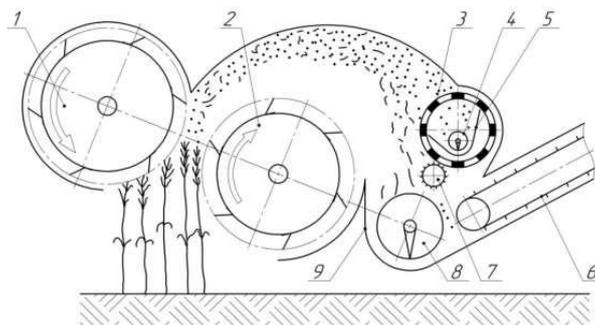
Пристрій для обмолоту рослин на корені: 1 – подаючий барабан; 2 – очисний барабан; 3 – циліндричний ґратчастий барабан; 4 – зерновий шнек; 5 – збірка прохідної фракції; 6 – похила камера; 7 – очистик; 8 – шнек; 9 – збірник.
